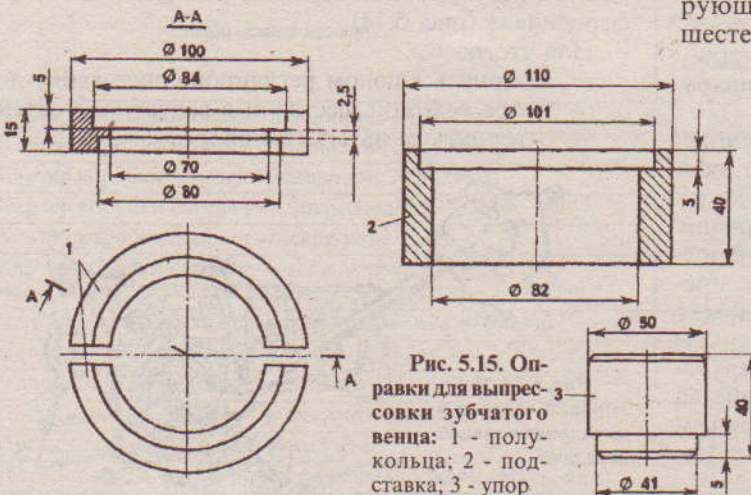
Оправки для выпрессовки зубчатого венца: 1 - полукольца; 2 - подставка; 3 - упор
